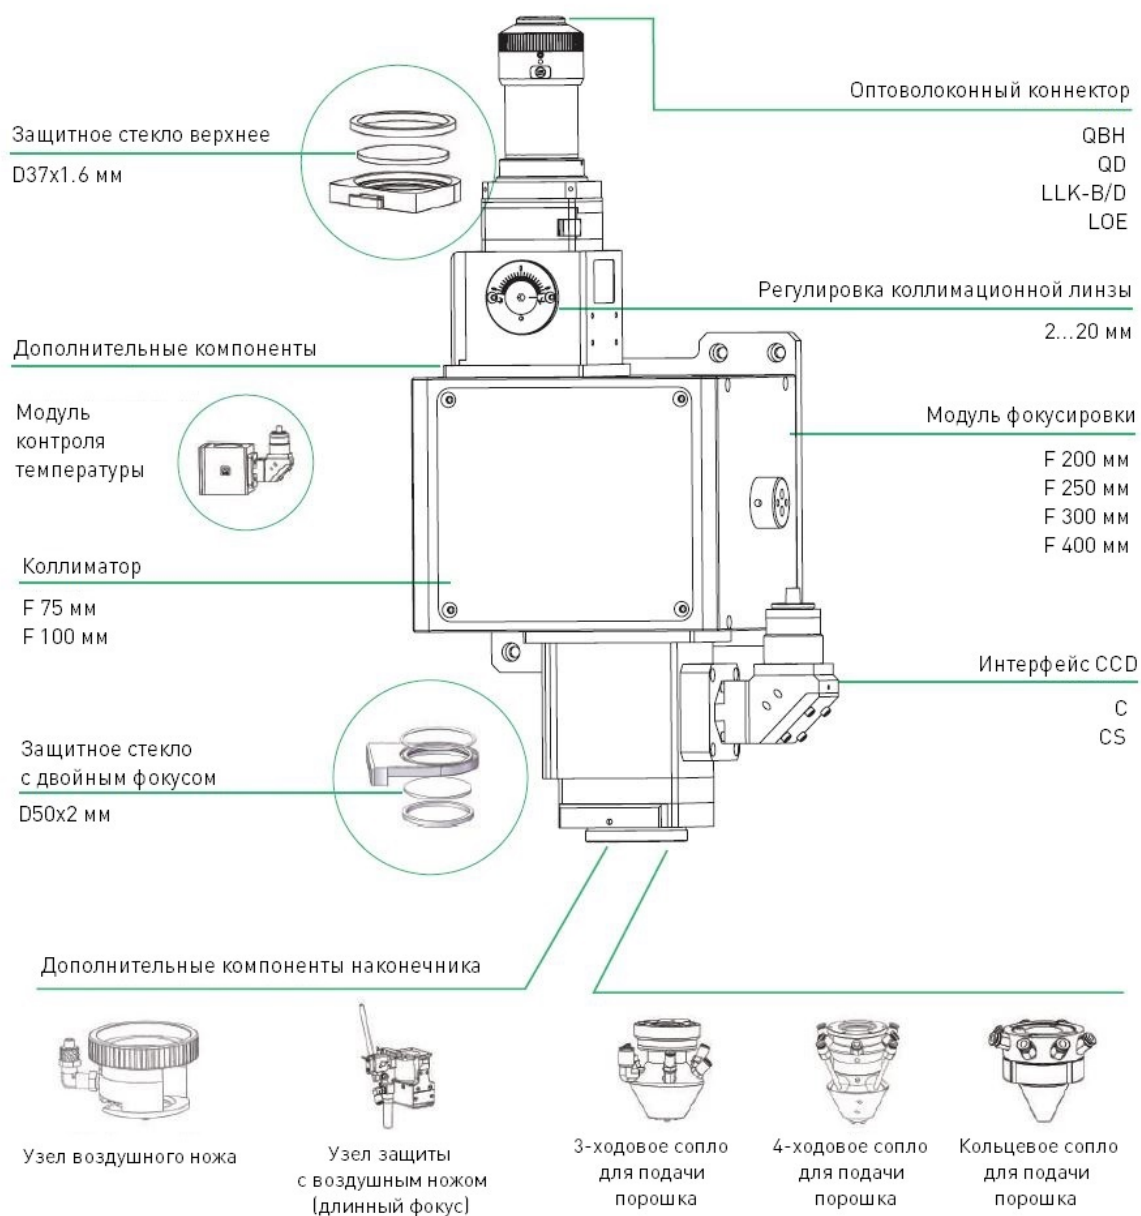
Схематическое изображение лазерной головки для сварки и наплавки VB106.
